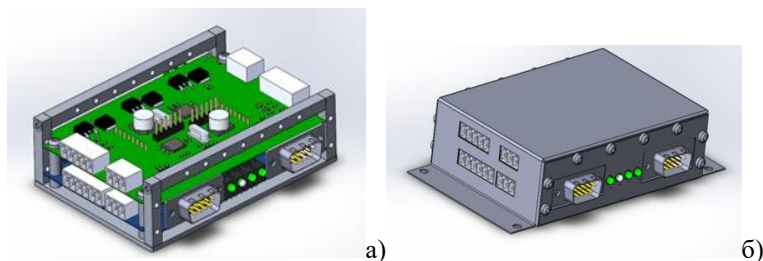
Общий вид блока без крышки (а) и в сборке (б)
